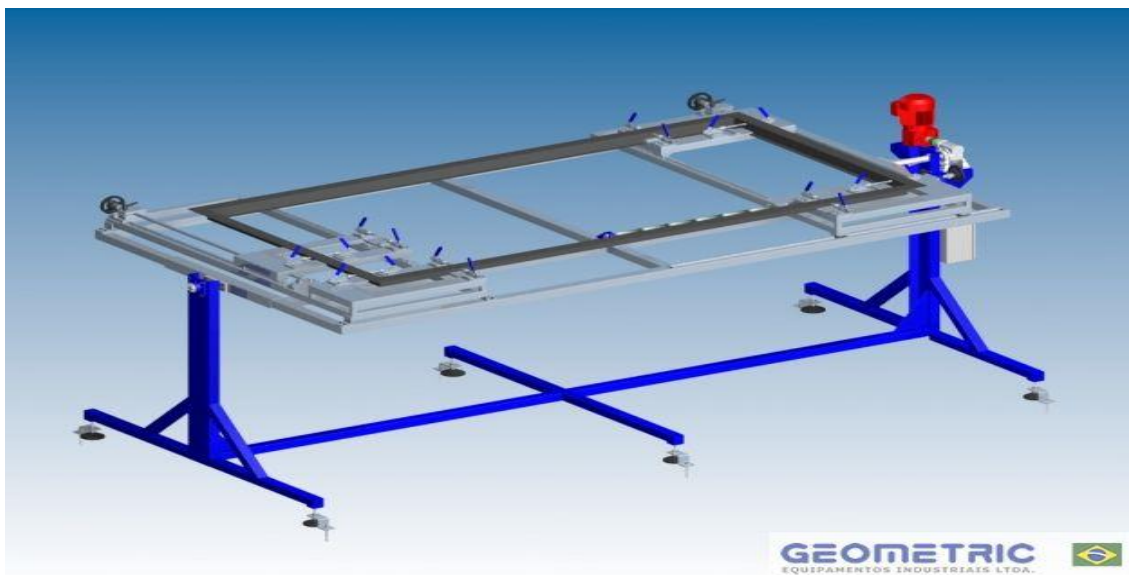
Dispositivo de solda sob Cavalete Giratório Fonte: Geometric
